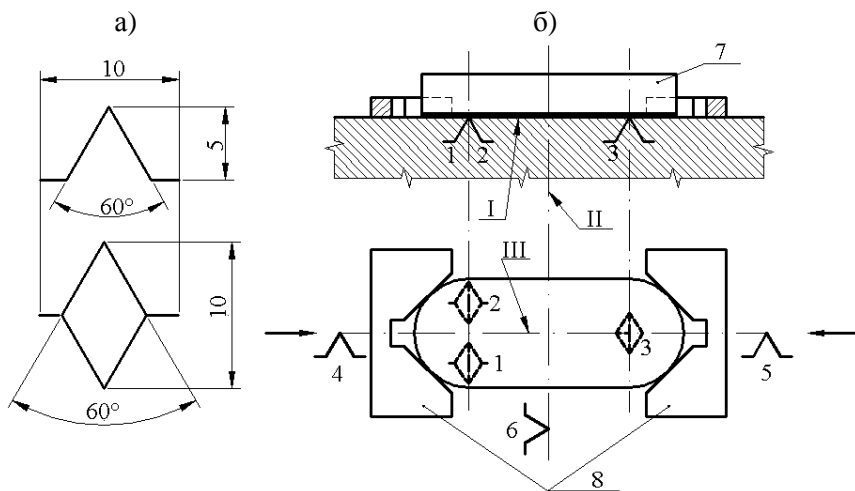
Условное изображение опорных точек (а) и установка заготовки в приспособление по комплексу баз с нанесенной схемой базирования (б): I – установочная явная база заготовки; II – направляющая скрытая база (ось) заготовки; 1...6 – опорные точки; 7 – заготовка; 8 – губки самоцентрирующих тисков
